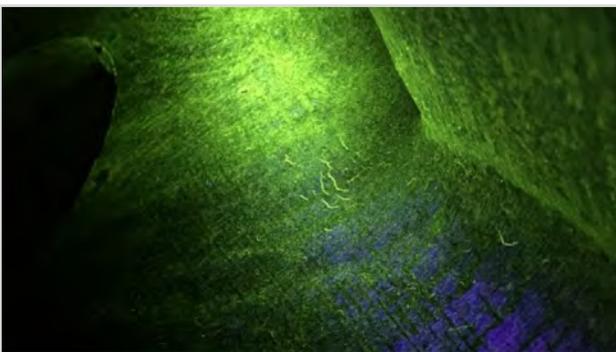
Haarrisse an der Gussoberfläche eines Bauteils aus niedrig legiertem Stahl
